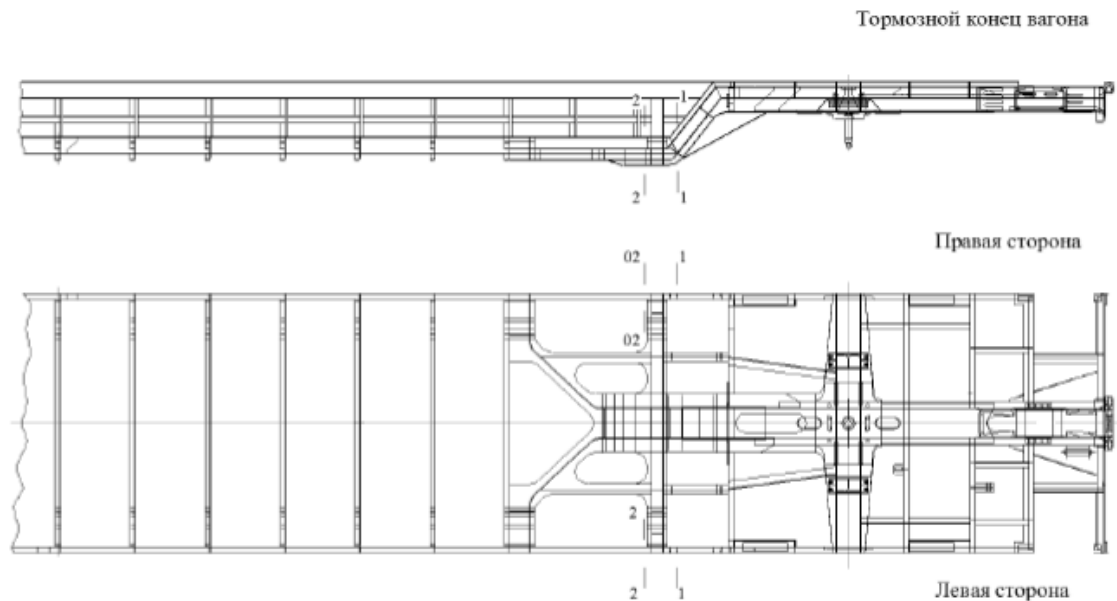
Загальний вигляд рами двоповерхового вагона
